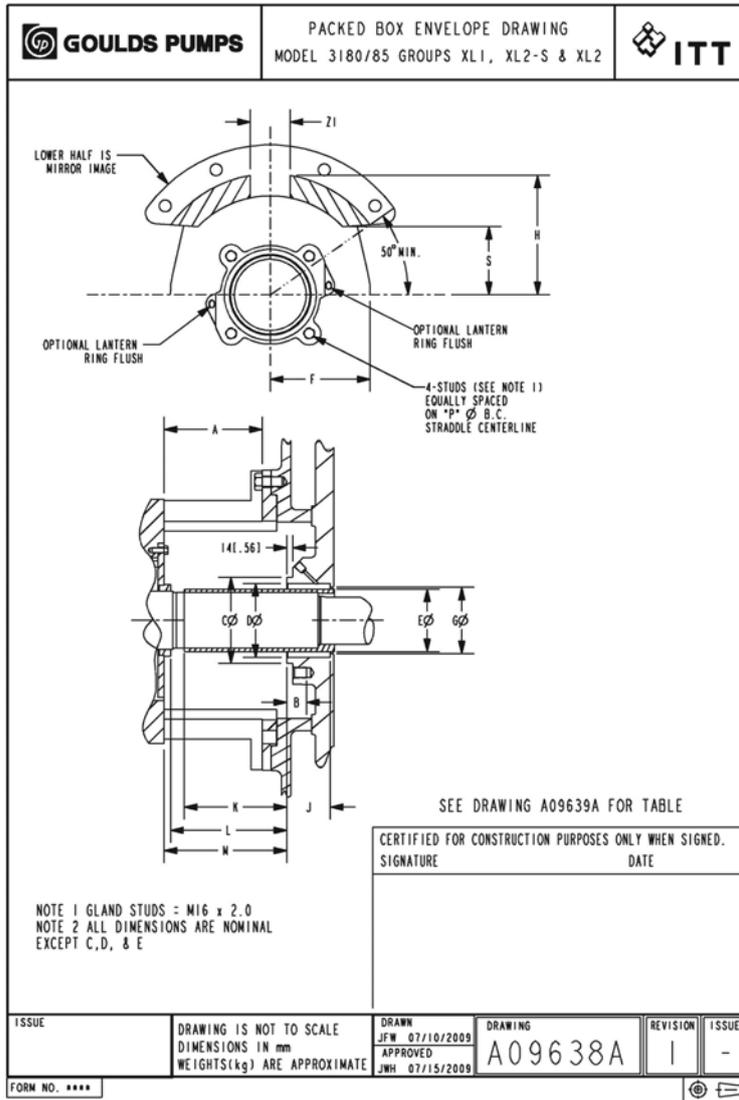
3180/3185 XL1, XL2-S и XL2 уплотнительная сальниковая коробка, чертеж A09638A, ред. 1, вып. -
